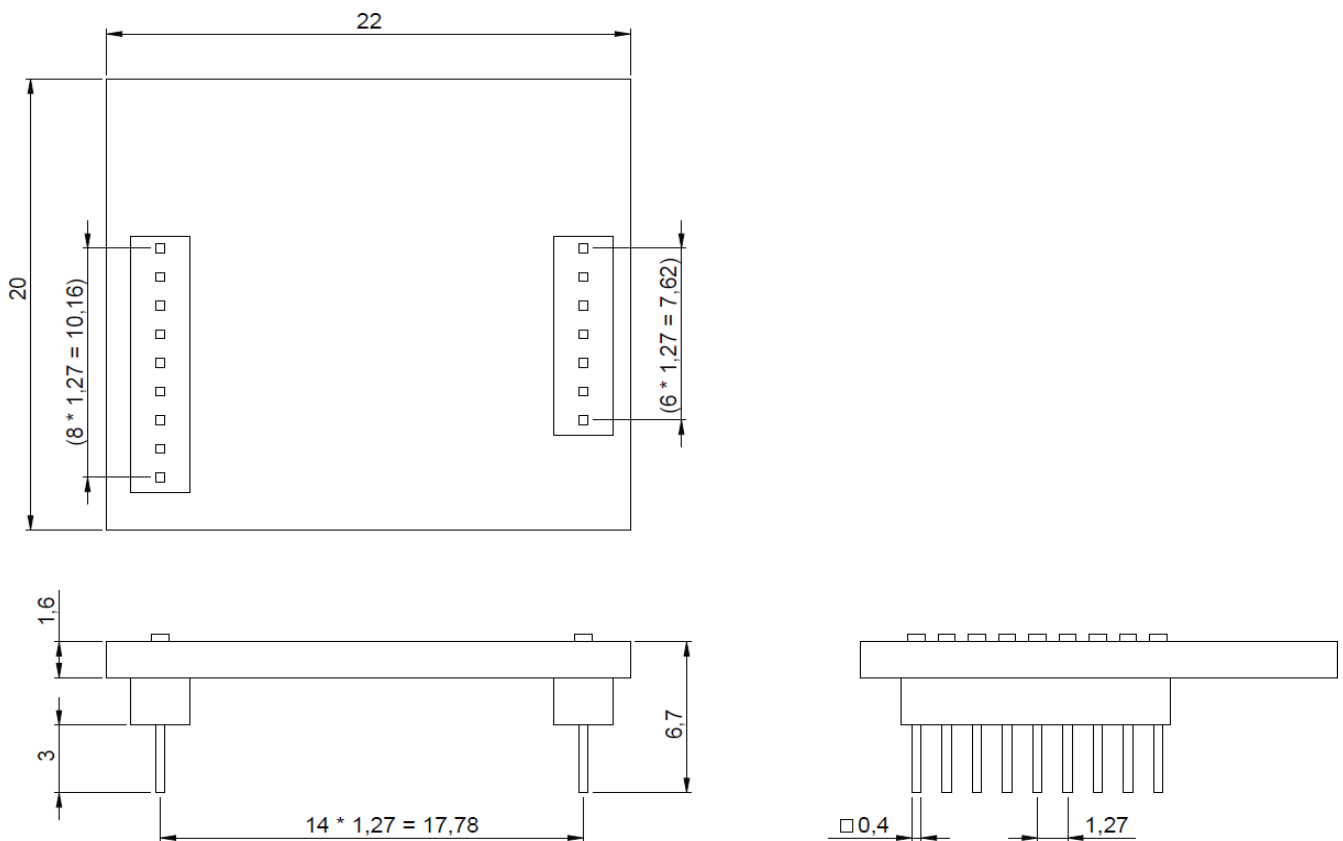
Dimensões da Shuttle Board 3.0 Multi-sensor
